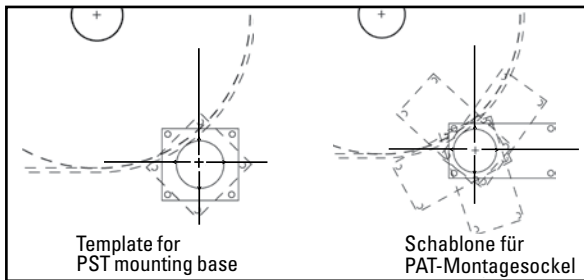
Center large template hole notches on pole center mark, rotate to desired angle and trace holes
